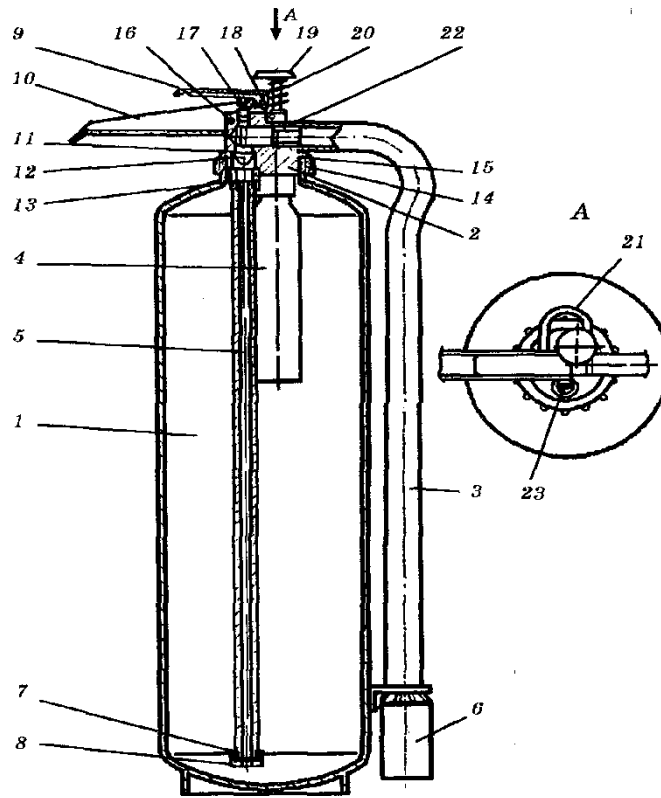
Вогнегасник повітряно-пінний ВПП-5: 1 – корпус; 2 – головка; 3 – рукав; 4 – балон з робочим газом; 5 – трубка сифонна; 6 – піногенератор; 7 – сітка; 8 – корпус фільтра; 9 – важіль керування клапаном; 10 – ручка; 11 – кільце ущільнювальне; 12 – клапан; 13 – перехідник; 14 – гайка накидна; 15 – кільце ущільнювальне; 16 – штифт; 17 – пружина; 18 – вісь; 19 – кнопка з голкою; 20 – пружина; 21 – запобіжна чека; 22 – кільце ущільнювальне; 23 – запобіжний клапан
